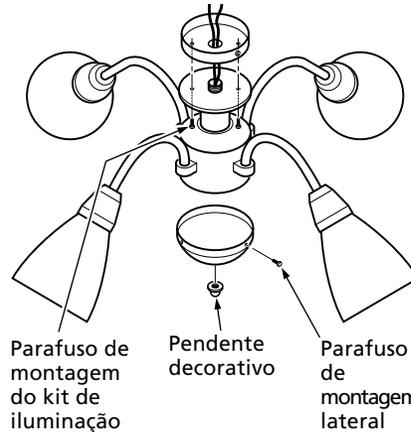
Kit de montagem por parafusos com tampa de fundo removível
